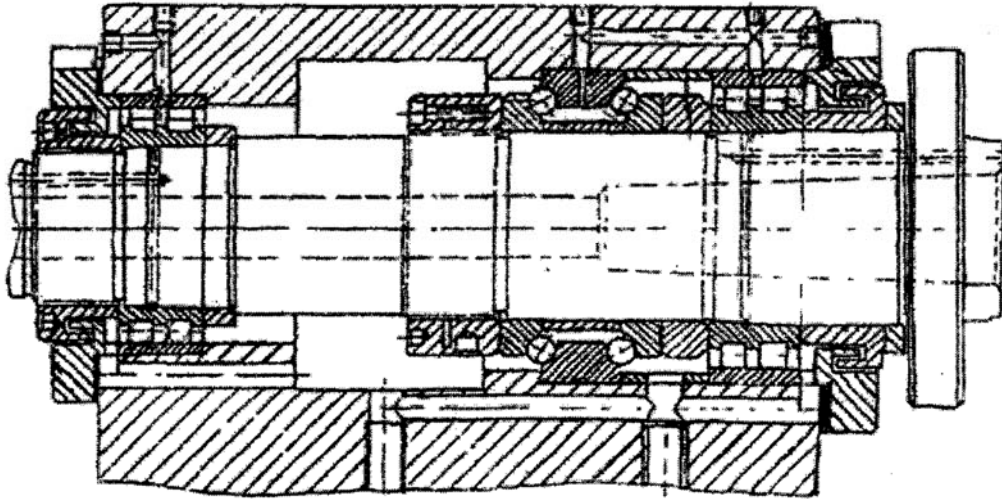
Шпиндельный узел станка с ЧПУ на роликоподшипниках типа 3182100 в обеих опорах и на шариковом упорно-радиальном типа 178000 в передней опоре
